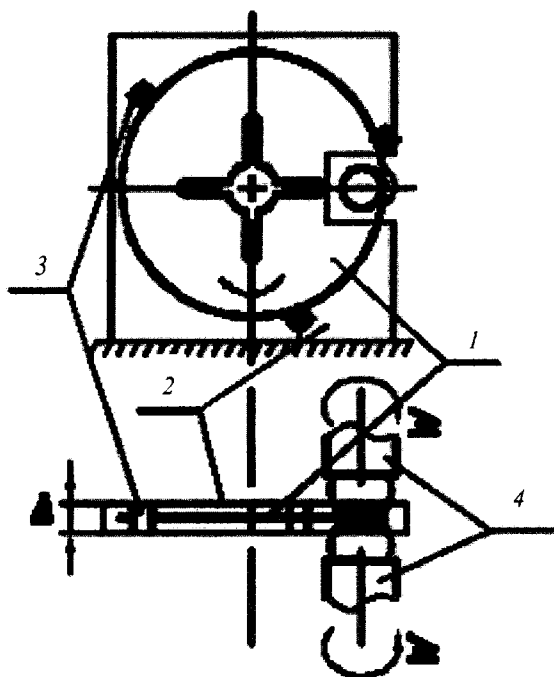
Схема бесцентрового шаржирования заготовок распиловочных дисков
